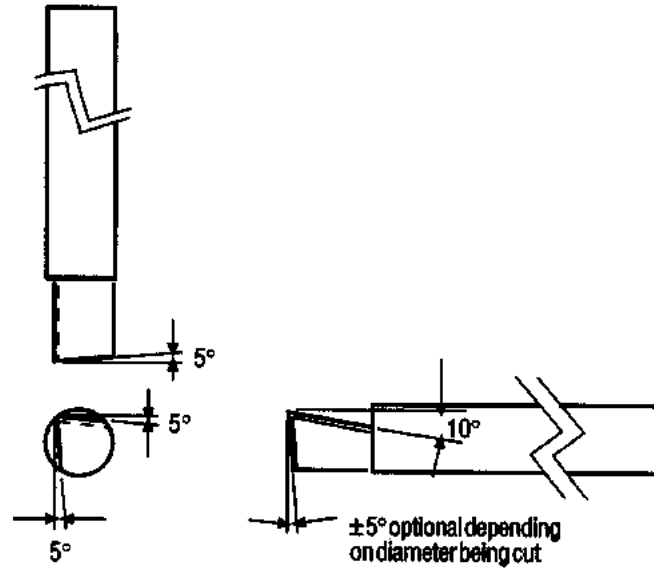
GEOMETRIE DE LA TETE D'OUTIL - POUCES (MM)
